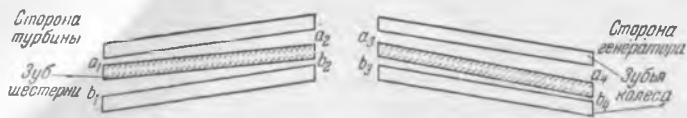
Схема расположения зубьев шестерни по отношению к зубьям колеса при центровке.
